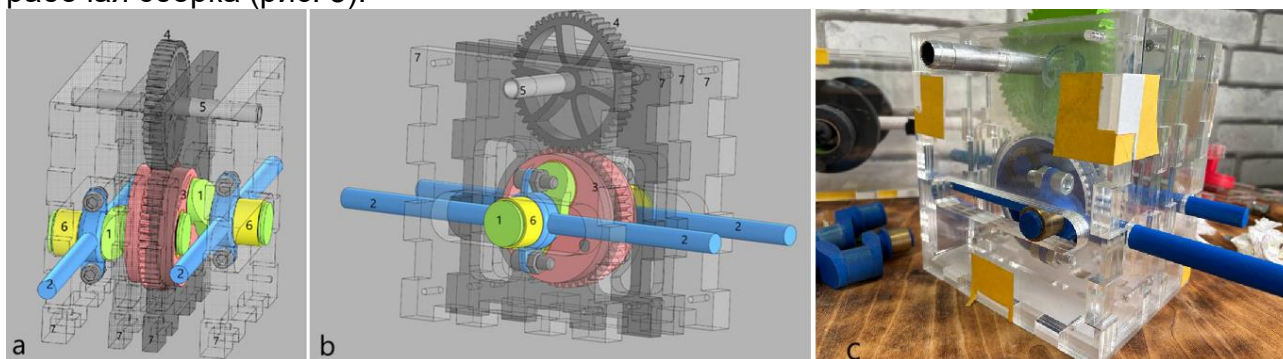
сборка 3D модели основного узла БШД с разных ракурсов (а и b). с – фото готового прототипа. 1 – Плечи коленвалов, 2 – Штоки, 3 – Маховик с зубчатым венцом, 4 – Шестерня вала двигателя, 5 – Вал двигателя, 6 – Втулки скольжения, 7 – Корпус.
